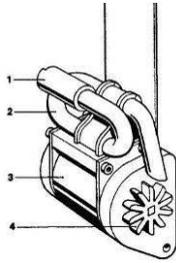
Пристрій для натягнення ремня безпеки з електричним керуванням від датчика прискорення: 1 - корпус з піропатроном, газовою камерою і поршнем; 2 – трубка; 3 - шків пасу безпеки; 4 - турбінне колесо з лопатками
